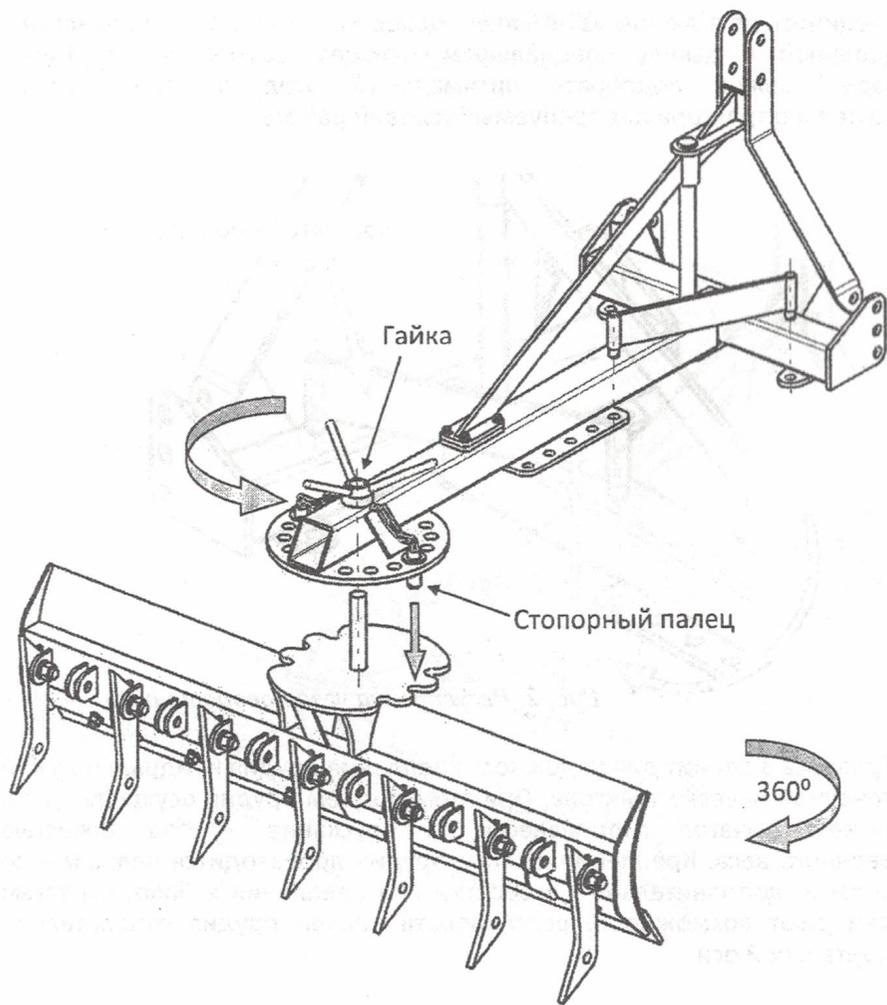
Регулировка угла атаки ножа лопаты с помощью поворотного кронштейна
